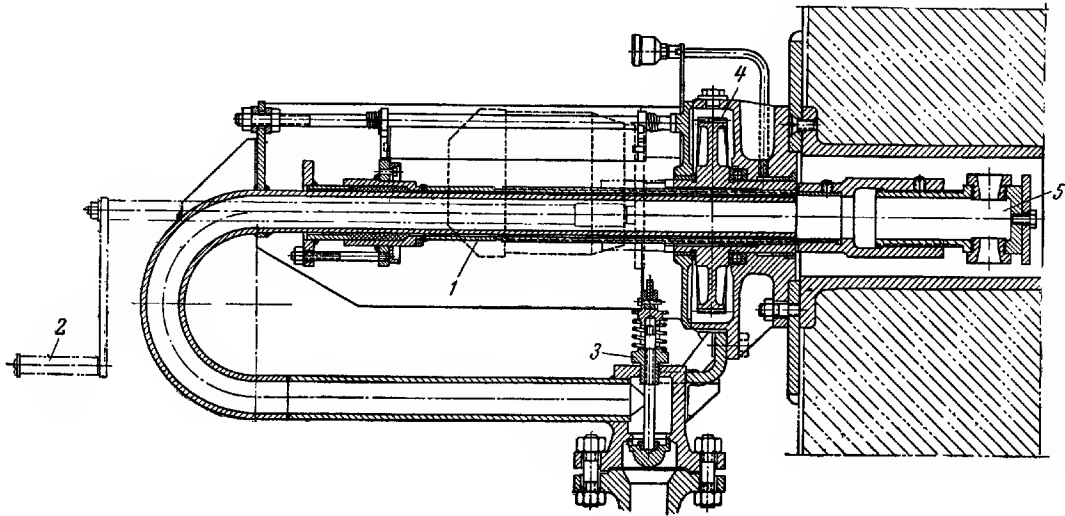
Обдувочный прибор Ильмарине-ЦКТИ для обдувки экранных поверхностей нагрева: 1 – электродвигатель; 2 – ручной привод; 3 – клапанный механизм; 4 – редуктор; 5 – сопловая головка
